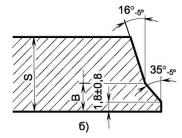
Форма разделки кромок труб для комбинированной сварки с применением Комплекса автоматической сварки
